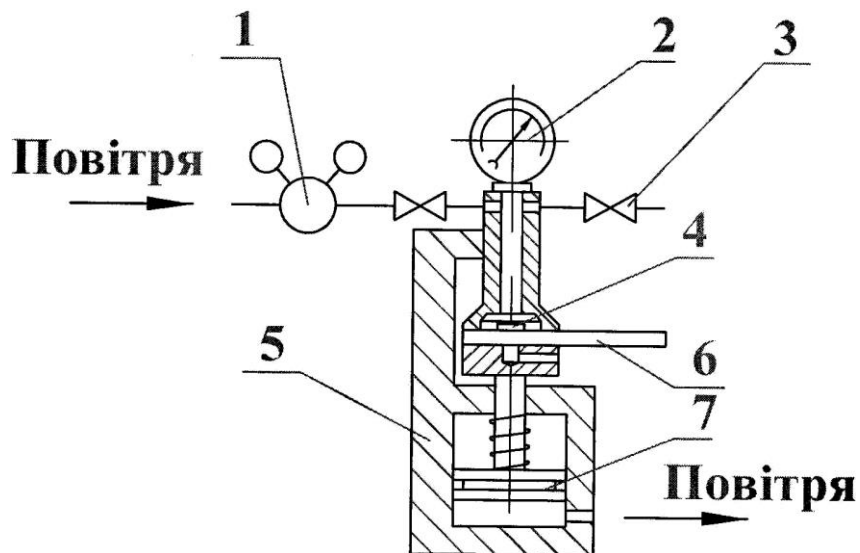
Схема пристосування для перевірки щільності прилягання клапана: 1 – редуктор; 2 – манометр; 3 – вентиль; 4 – клапан; 5 – корпус; 6 – клапанна дошка, 7 – поршень
